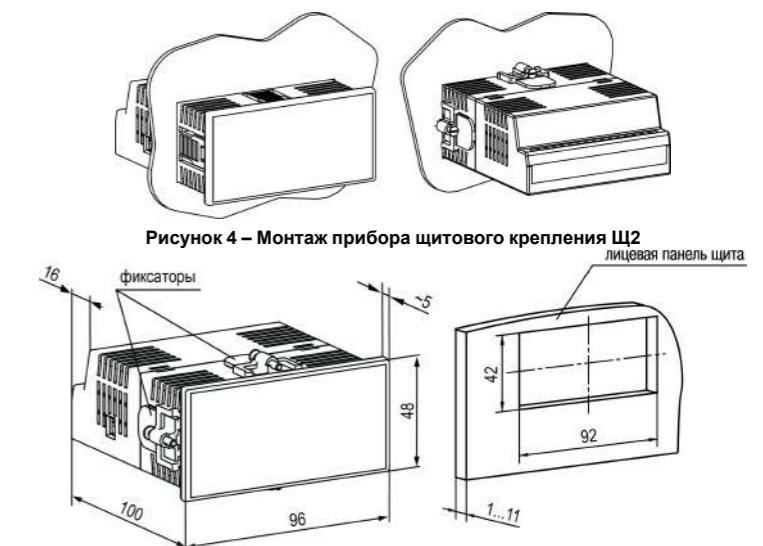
Монтаж прибора щитового крепления Щ2
